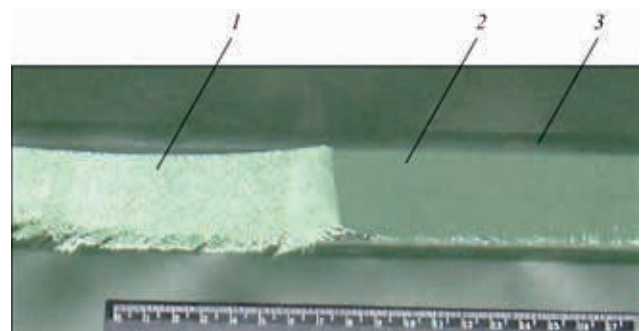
Якісний зварний шов ламінованої тканини Unisol 950 після випробування на відрив з'єднувальної стрічки: 1 – відірвана стрічка з оголеним кордом; 2 – зварний шов; 3 – зона термічного впливу біля шва
